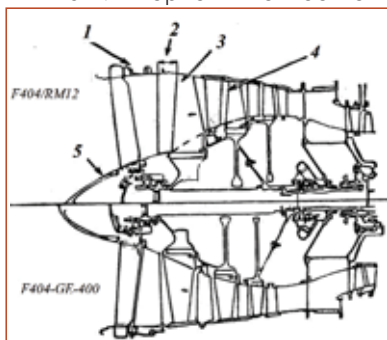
Изменения в конструкции вентилятора двигателя VM12
